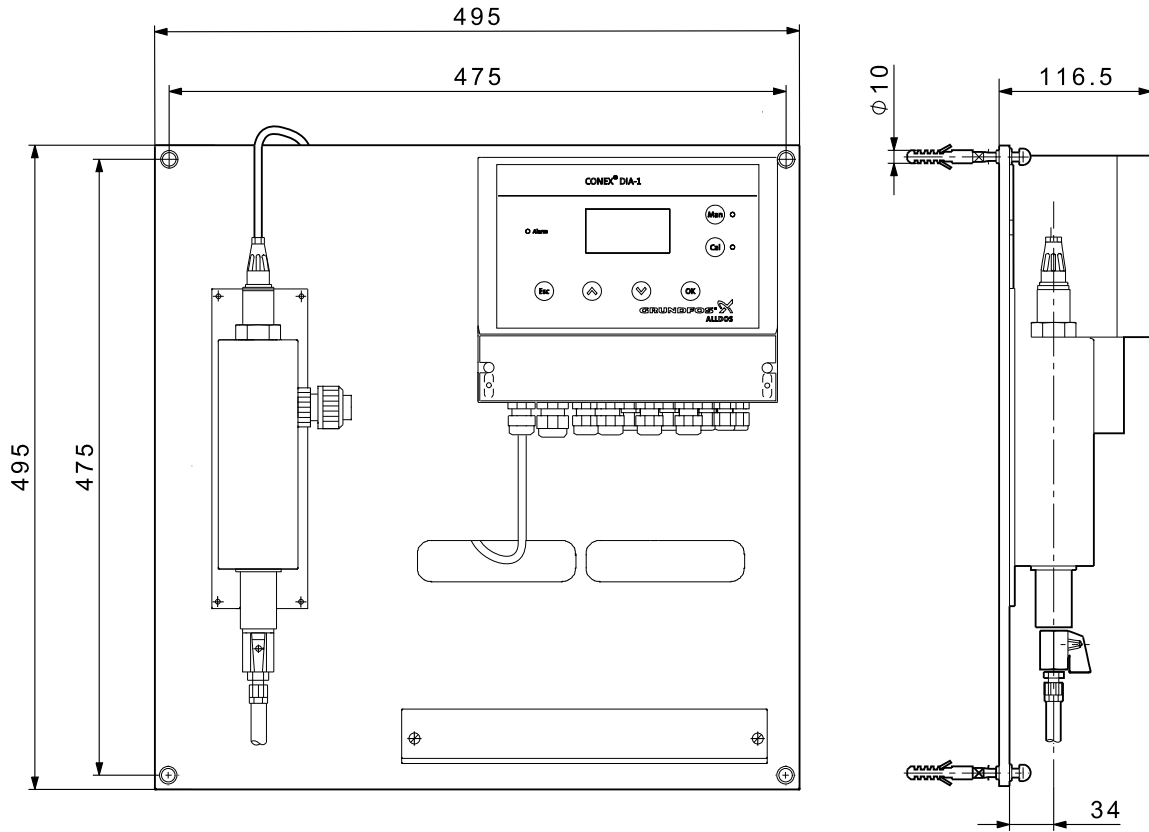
Maßzeichnung / Bohrbild für Conex® DIA-1-A PA/HP / Conex® DIA-2Q-A PA/HP
